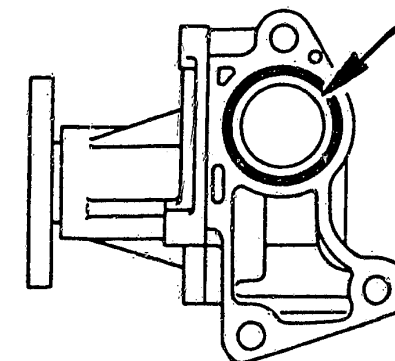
An dem gegen den Motorblock gerichteten Gehäuseteil der Wasserpumpe ist vor dem Anbau auf einer Breite von 2...3mm Dichtungsmasse aufzutragen.
